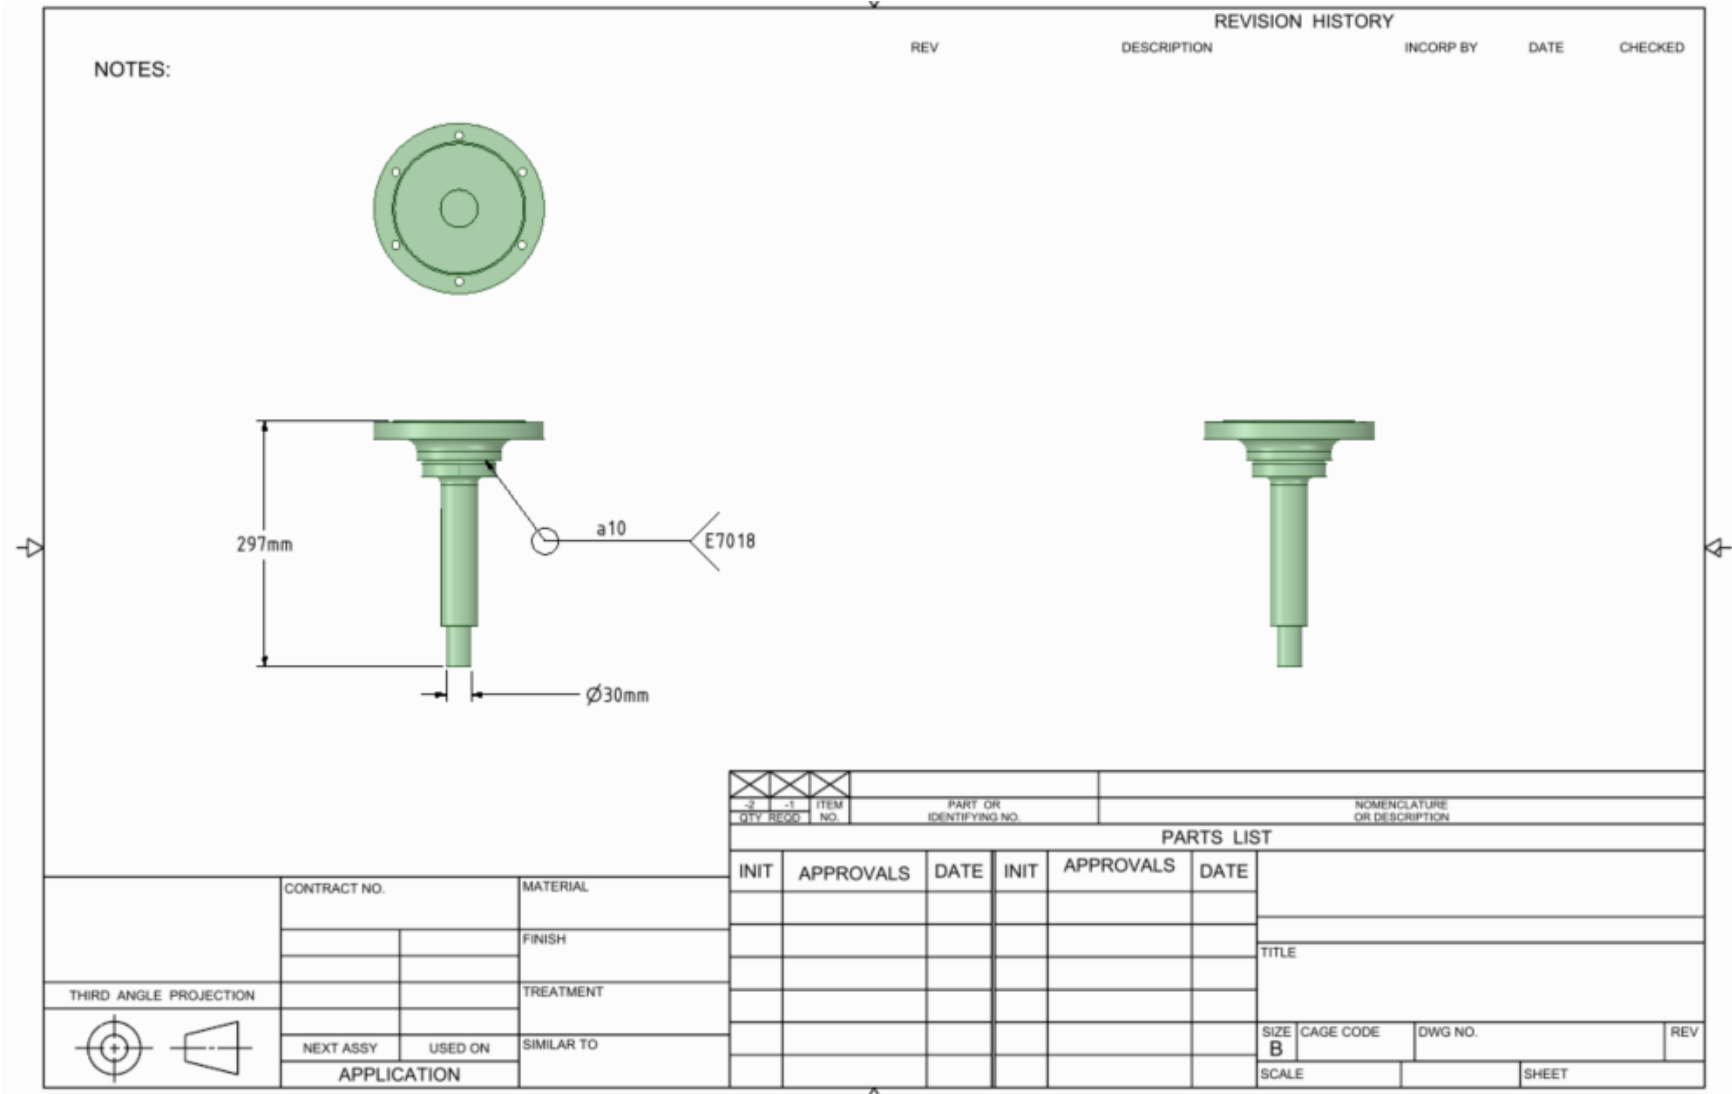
Planos de fabricación eje ensamblado. Fuente: Elaboración propia.
